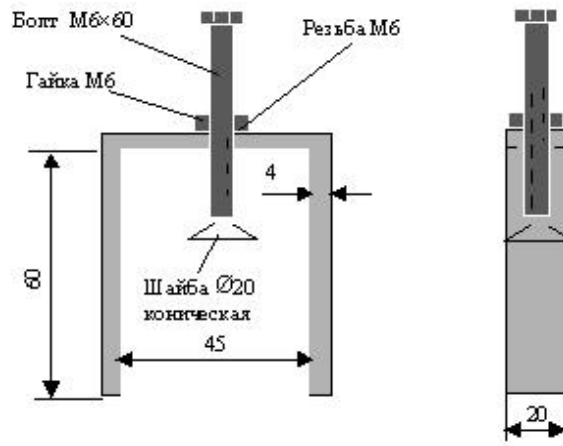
Скоба для крепления накладных ПЭА на трубопроводе
